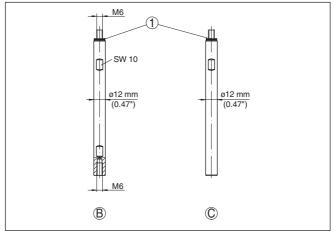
Componentes de varilla - ø 12 mm (0.47 in)
